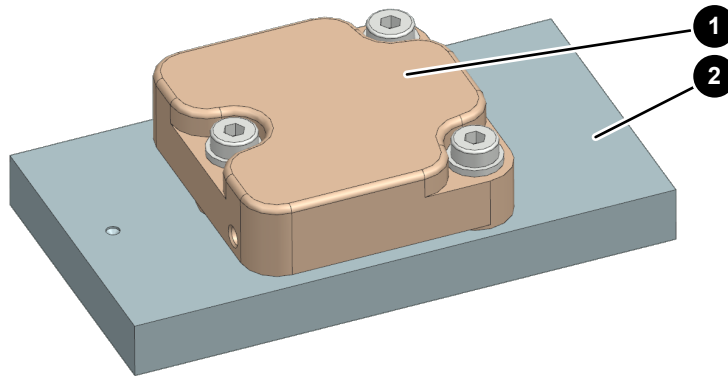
Montage des Pulsotronic-Sensors auf der GFK-Montageplatte
